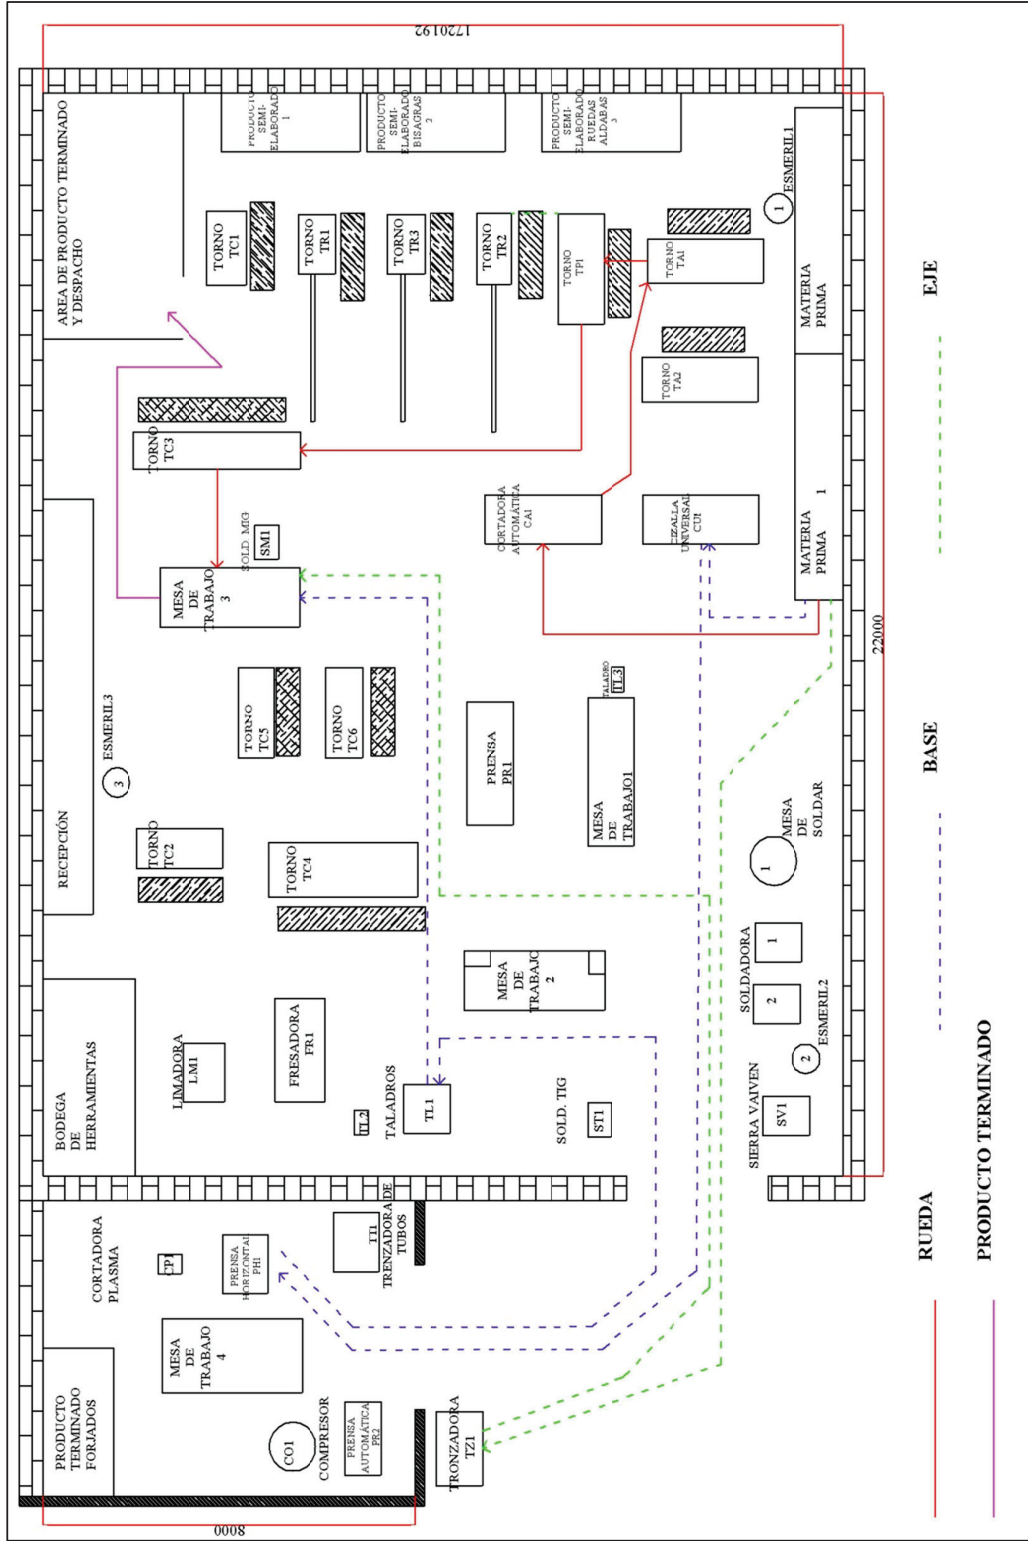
Disposición propuesta para los centros de trabajo -ruedas con base horizontal
